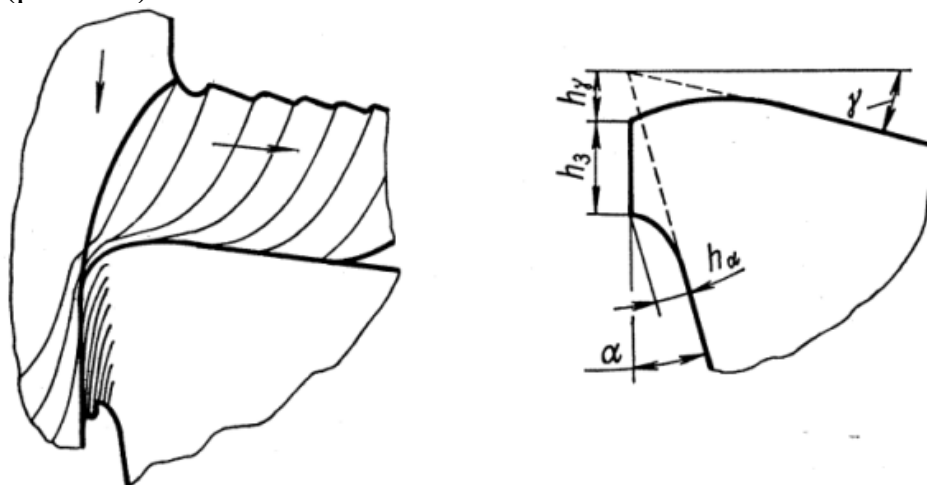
Пластические разрушения режущей части инструментов
